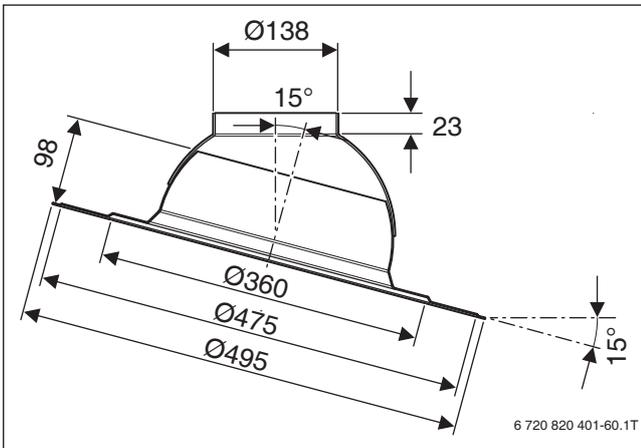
Flachdach-Klebeflansch für DN 80/125 (Maße in mm)
